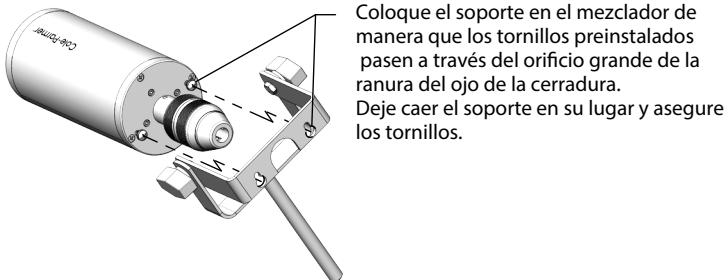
Instalación del soporte de montaje de inclinación ajustable
